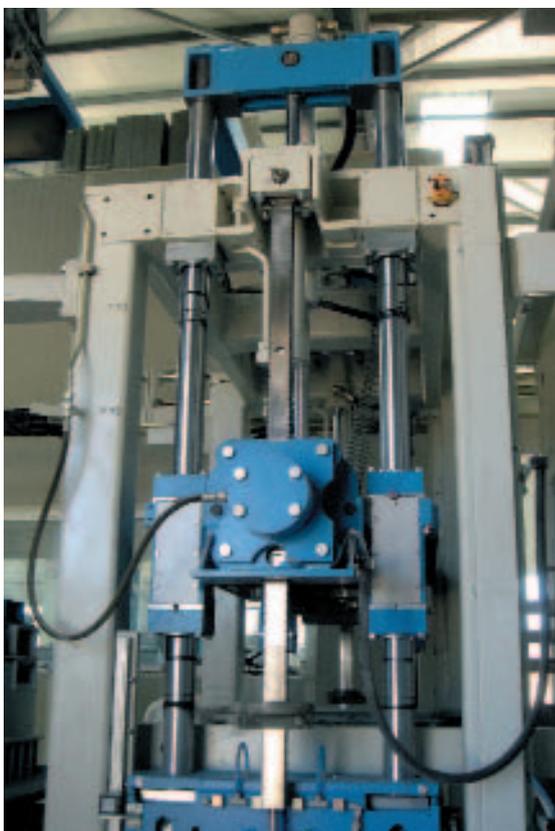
Транспортировка форм вызывает особый интерес: опора направляющей формы по стойкам не скользит, а наоборот, стойки перемещаются по конструкции машины.
